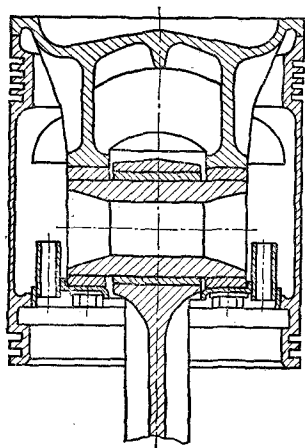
Поршень быстрогоходного судового двигателя GMC
